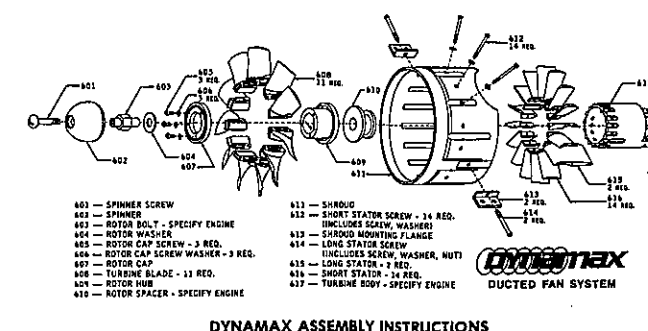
Montagezeichnung des Dynamax Impellers
